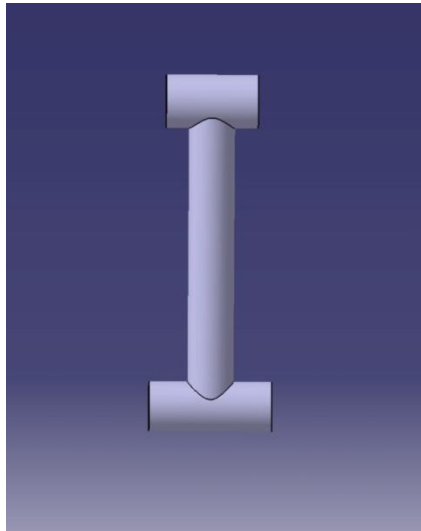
Tubo a dimensionar, modelado em CATIA.
